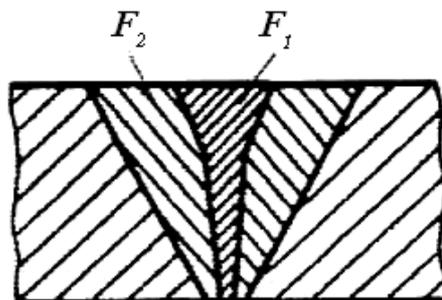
Формы проплавления при дуговой (F_2) и электронно-лучевой (F_1) сварке
